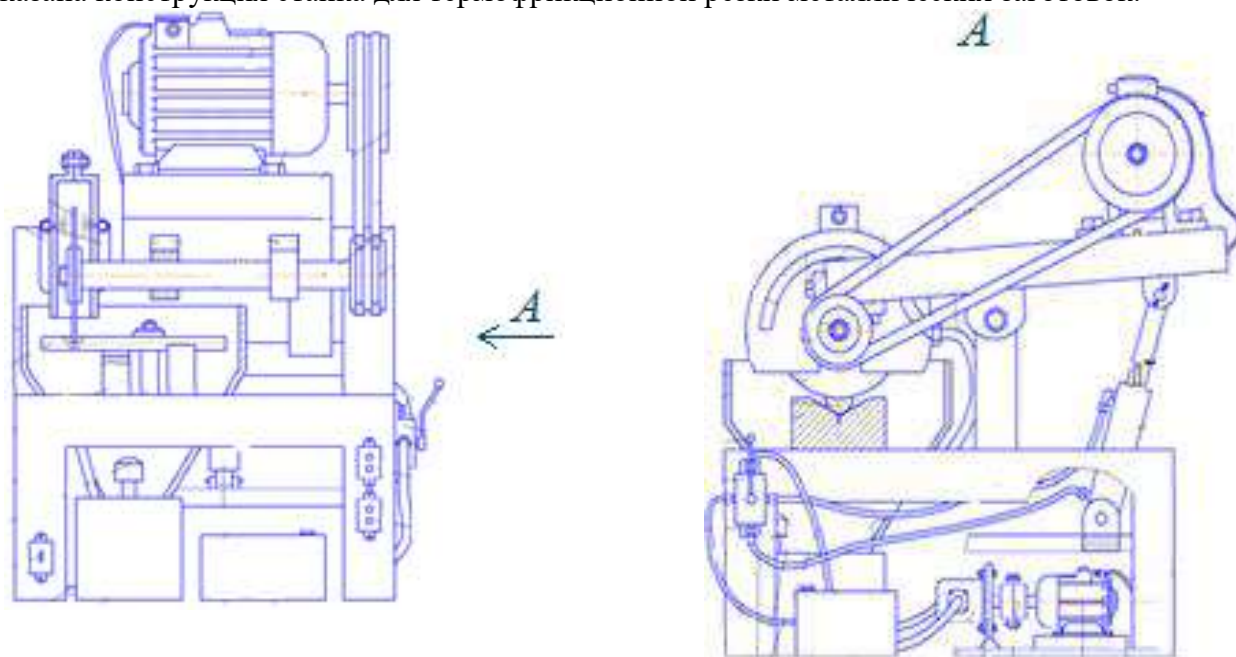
Станок для термофрикционной резки металлических заготовок
